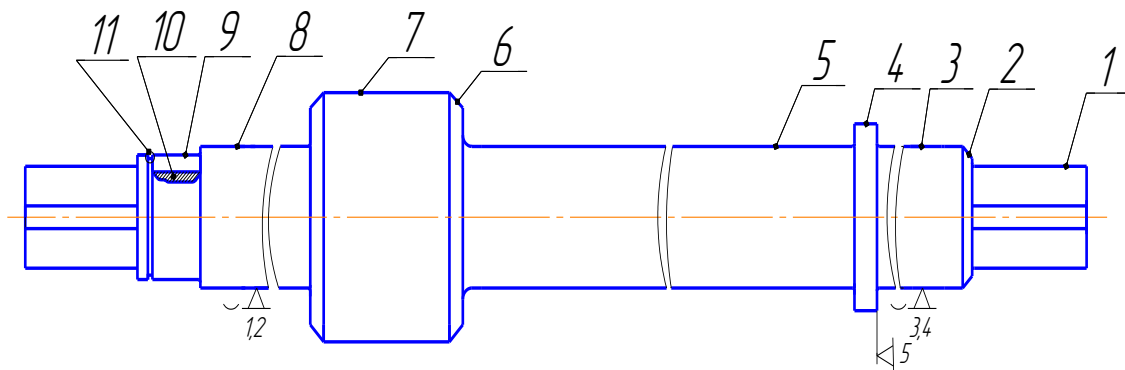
Ескіз деталі з нумерацією поверхонь
